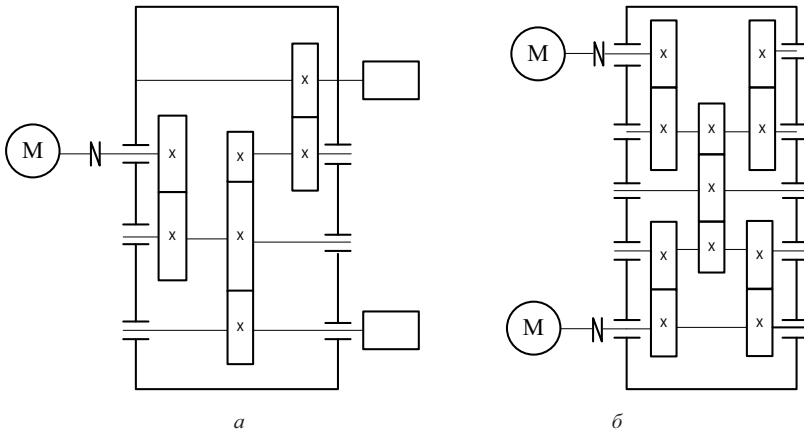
Привод с дублированными кинематическими элементами:
